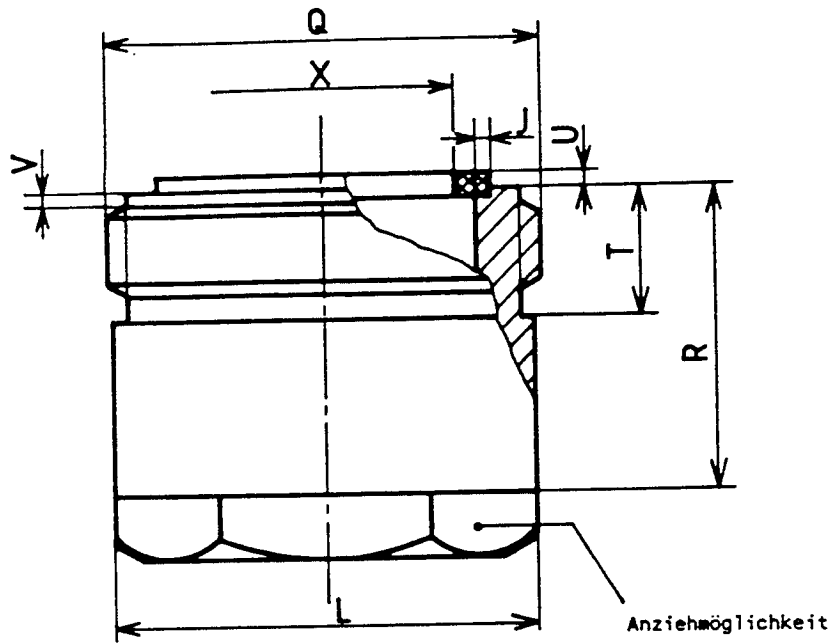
Strahlregler mit Anschluß mit Außengewinde
